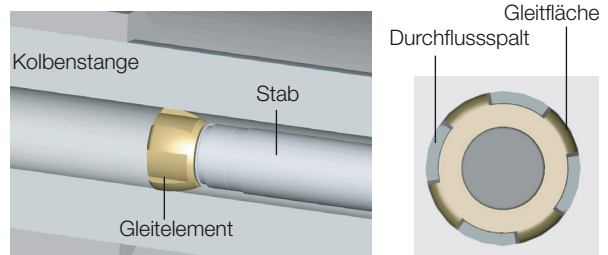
Detailansicht und Draufsicht Gleitelement
